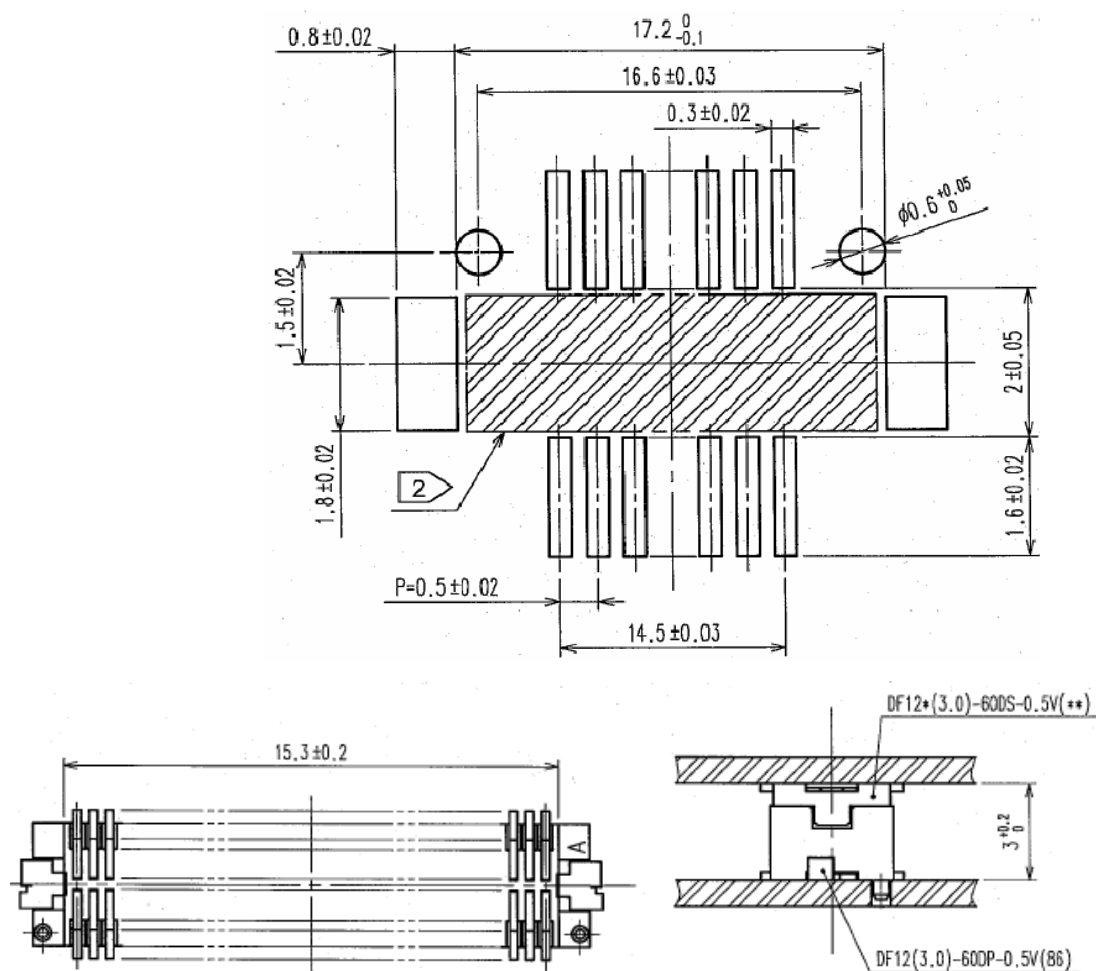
MC703 模块用户接口板上使用的连接器焊盘尺寸 (单位: mm)
